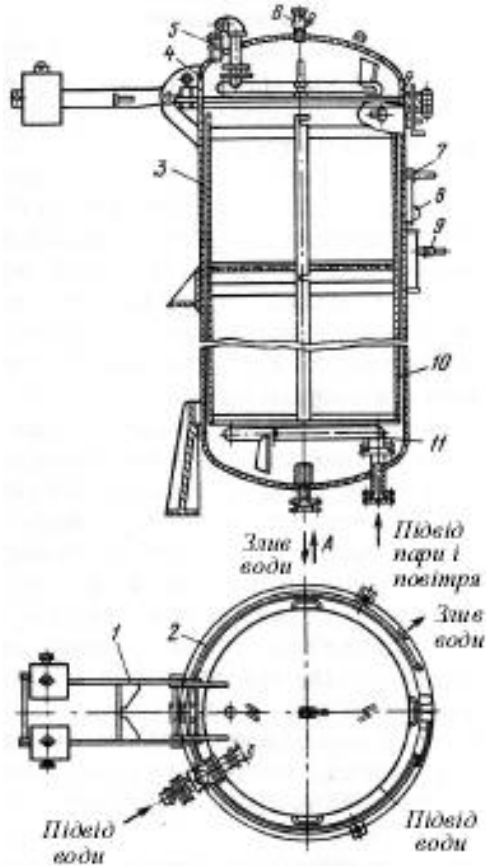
Вертикальний автоклав 1 - зрівноважувальний пристрій; 2 - затискач; 3 - корпус; 4 - кришка; 5 - запобіжний клапан; 6 - контрольно-спусковий кран; 7 - термометр; 8 - манометр; 9 - програмний регулятор; 10 - корзина; 11 - кільцевий барботер
